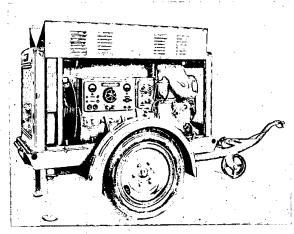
Diesel-Schweißaggregat für 300 A (Schorch-Deutz)
